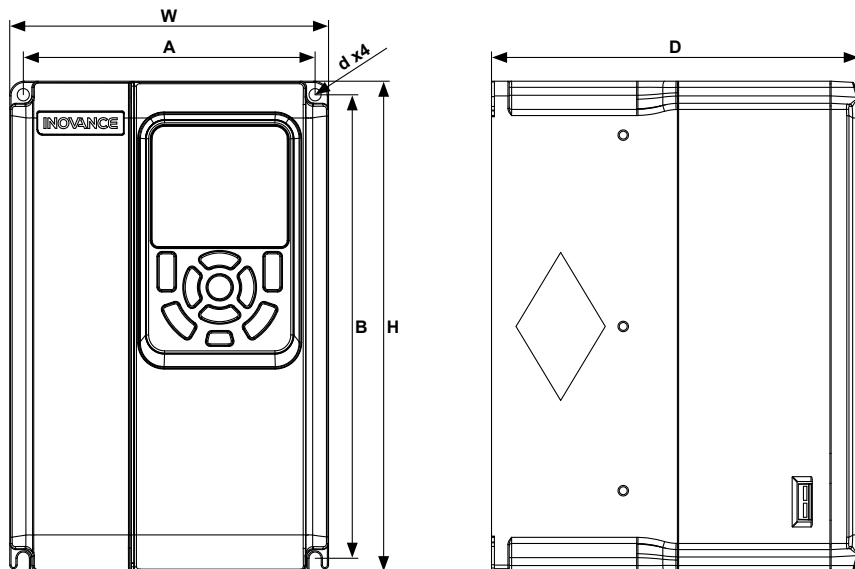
Внешний вид типоразмеров Т1 - Т4
